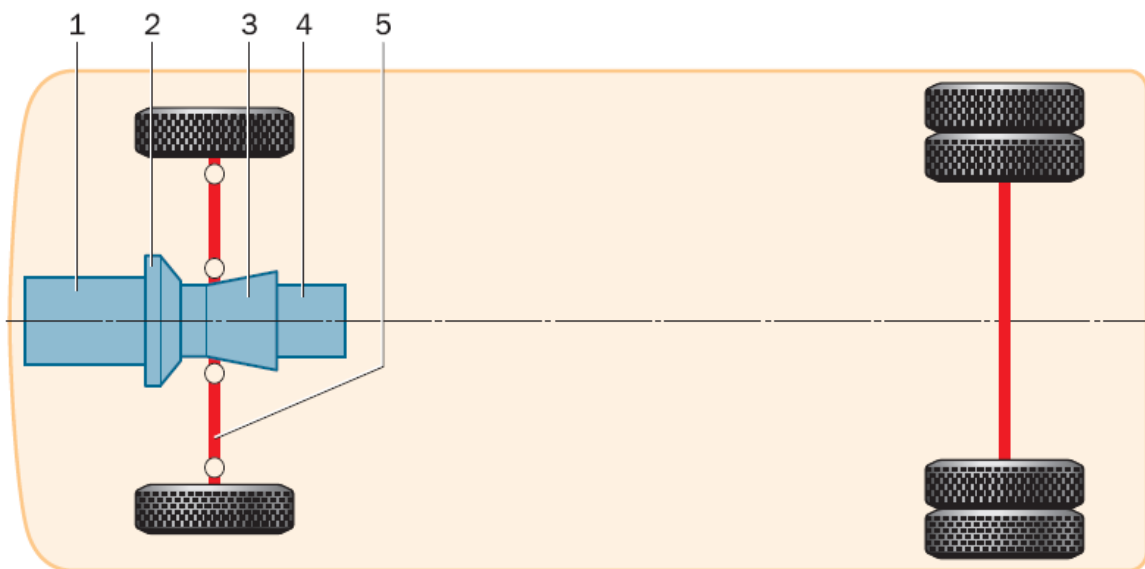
Передньопривідна компоновка з поздовжнім розташуванням двигуна: 1 – двигун; 2 – зчеплення; 3 – головна передача; 4 – коробка передач; 5 – вал приводу ведучих коліс
